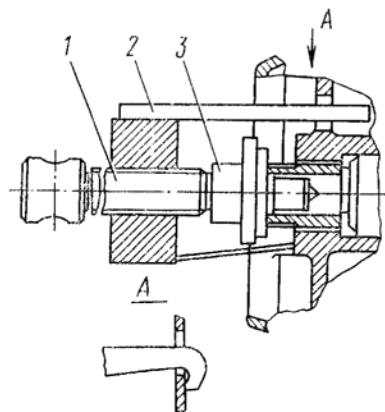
Съёмник рулевого колеса: 1 - винт; 2 - захват; 3 - наконечник
